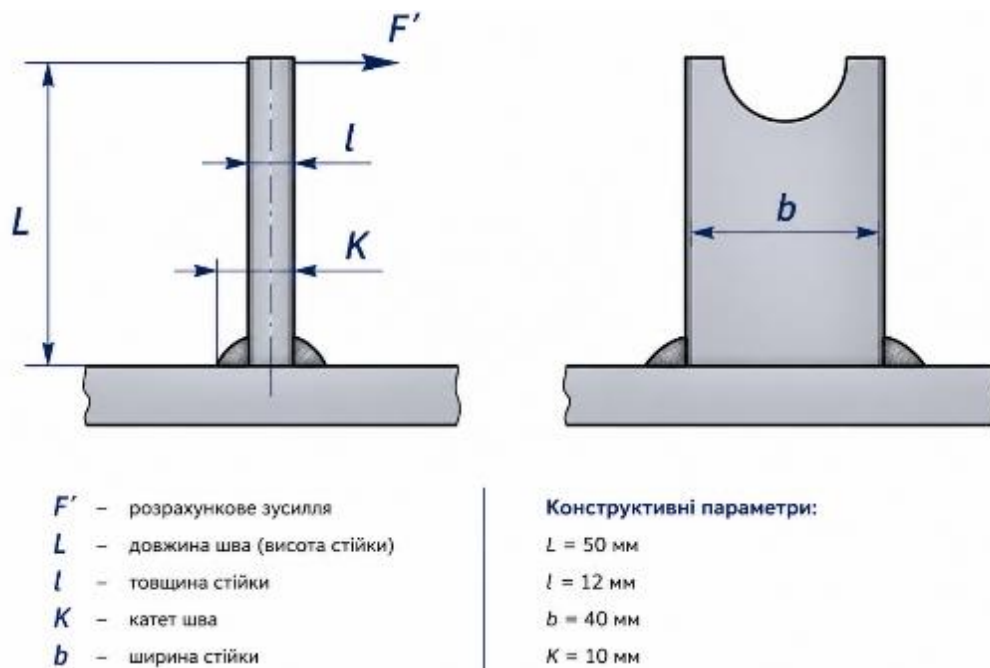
Схема перевірки міцності зварного з'єднання
